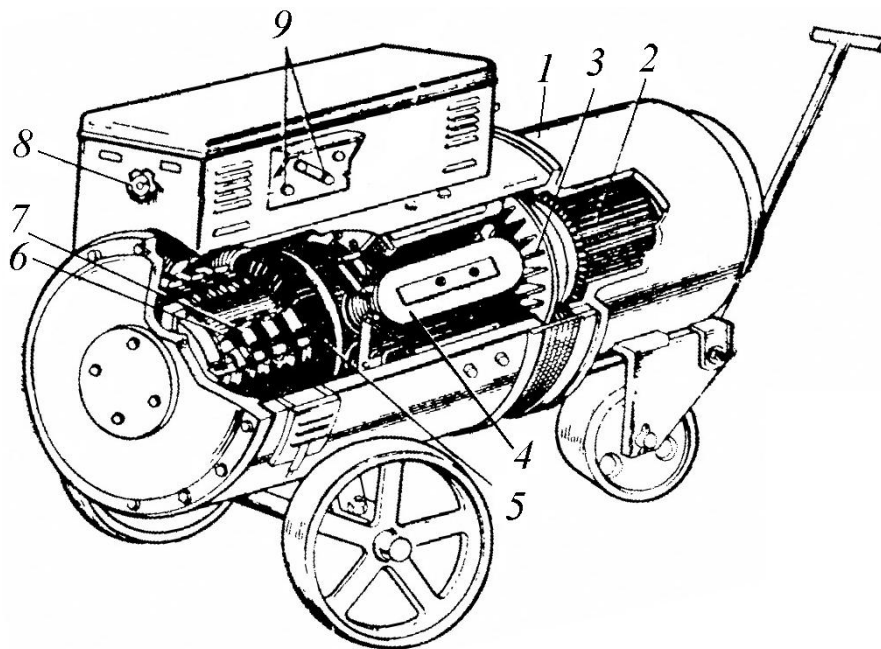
Общий вид сварочного преобразователя ПСО-300: 1 – корпус; 2 – электродвигатель; 3 – вентилятор; 4 – катушки полюсов; 5 – якорь; 6 – коллектор; 7 – щетки токосъемника; 8 – маховичок регулирования тока; 9 – зажимы подключения сварочных проводов
